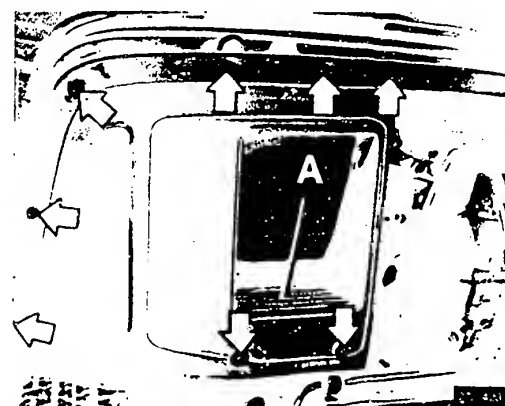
Die Luftführung (Pfeile) und der Ölkühler müssen abgebaut werden, um zum Alternator oder Anlasser zu gelangen.
